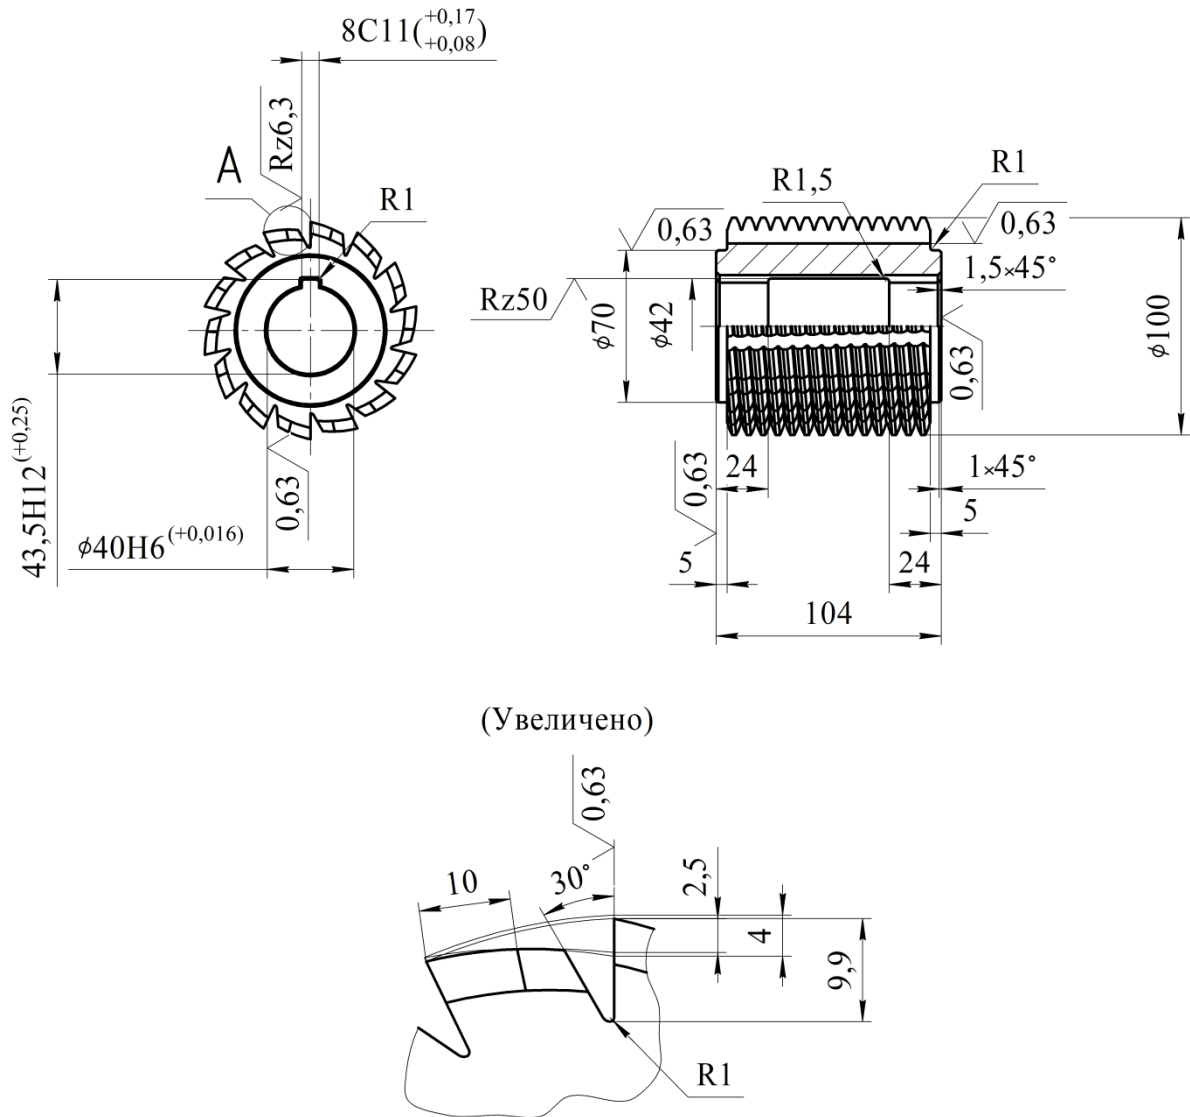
Конструкция червячной однозаходной фрезы с прогрессивной схемой резания
